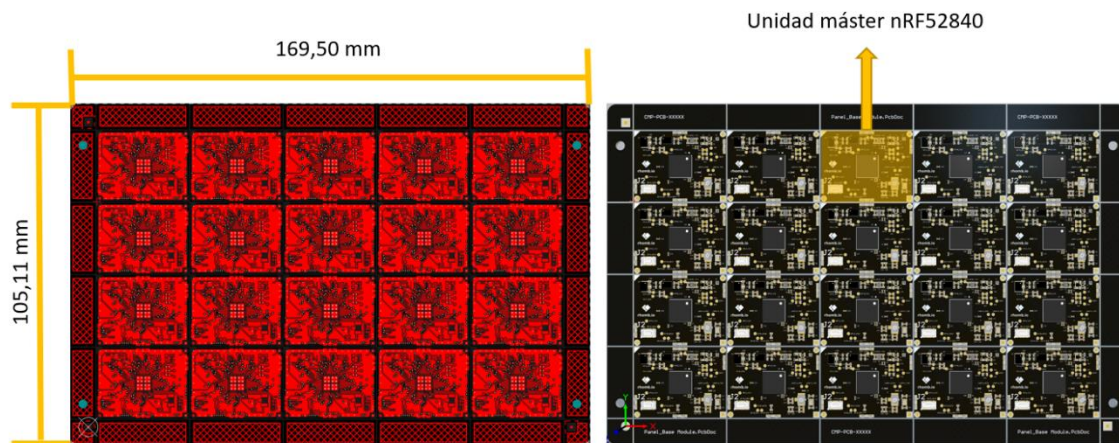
Vista en 2D (izquierda) y 3D (derecha) del panel PCB para la fabricación de 20 unidades del modulo máster nRF52840.
